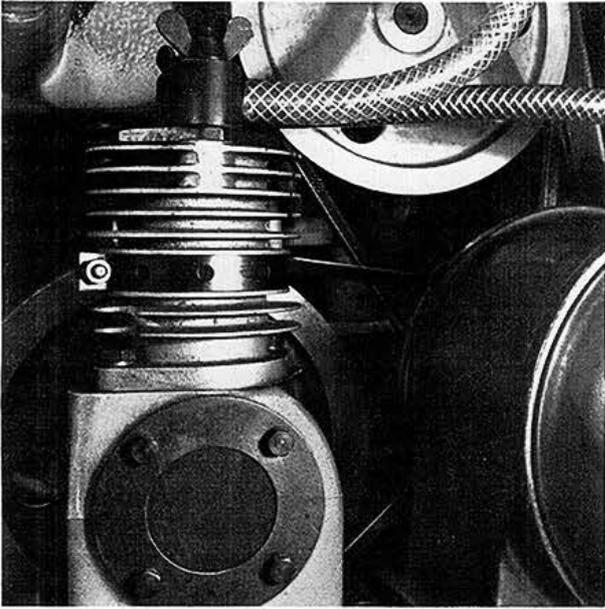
Kompressor im Grundgestell einer Maschine
